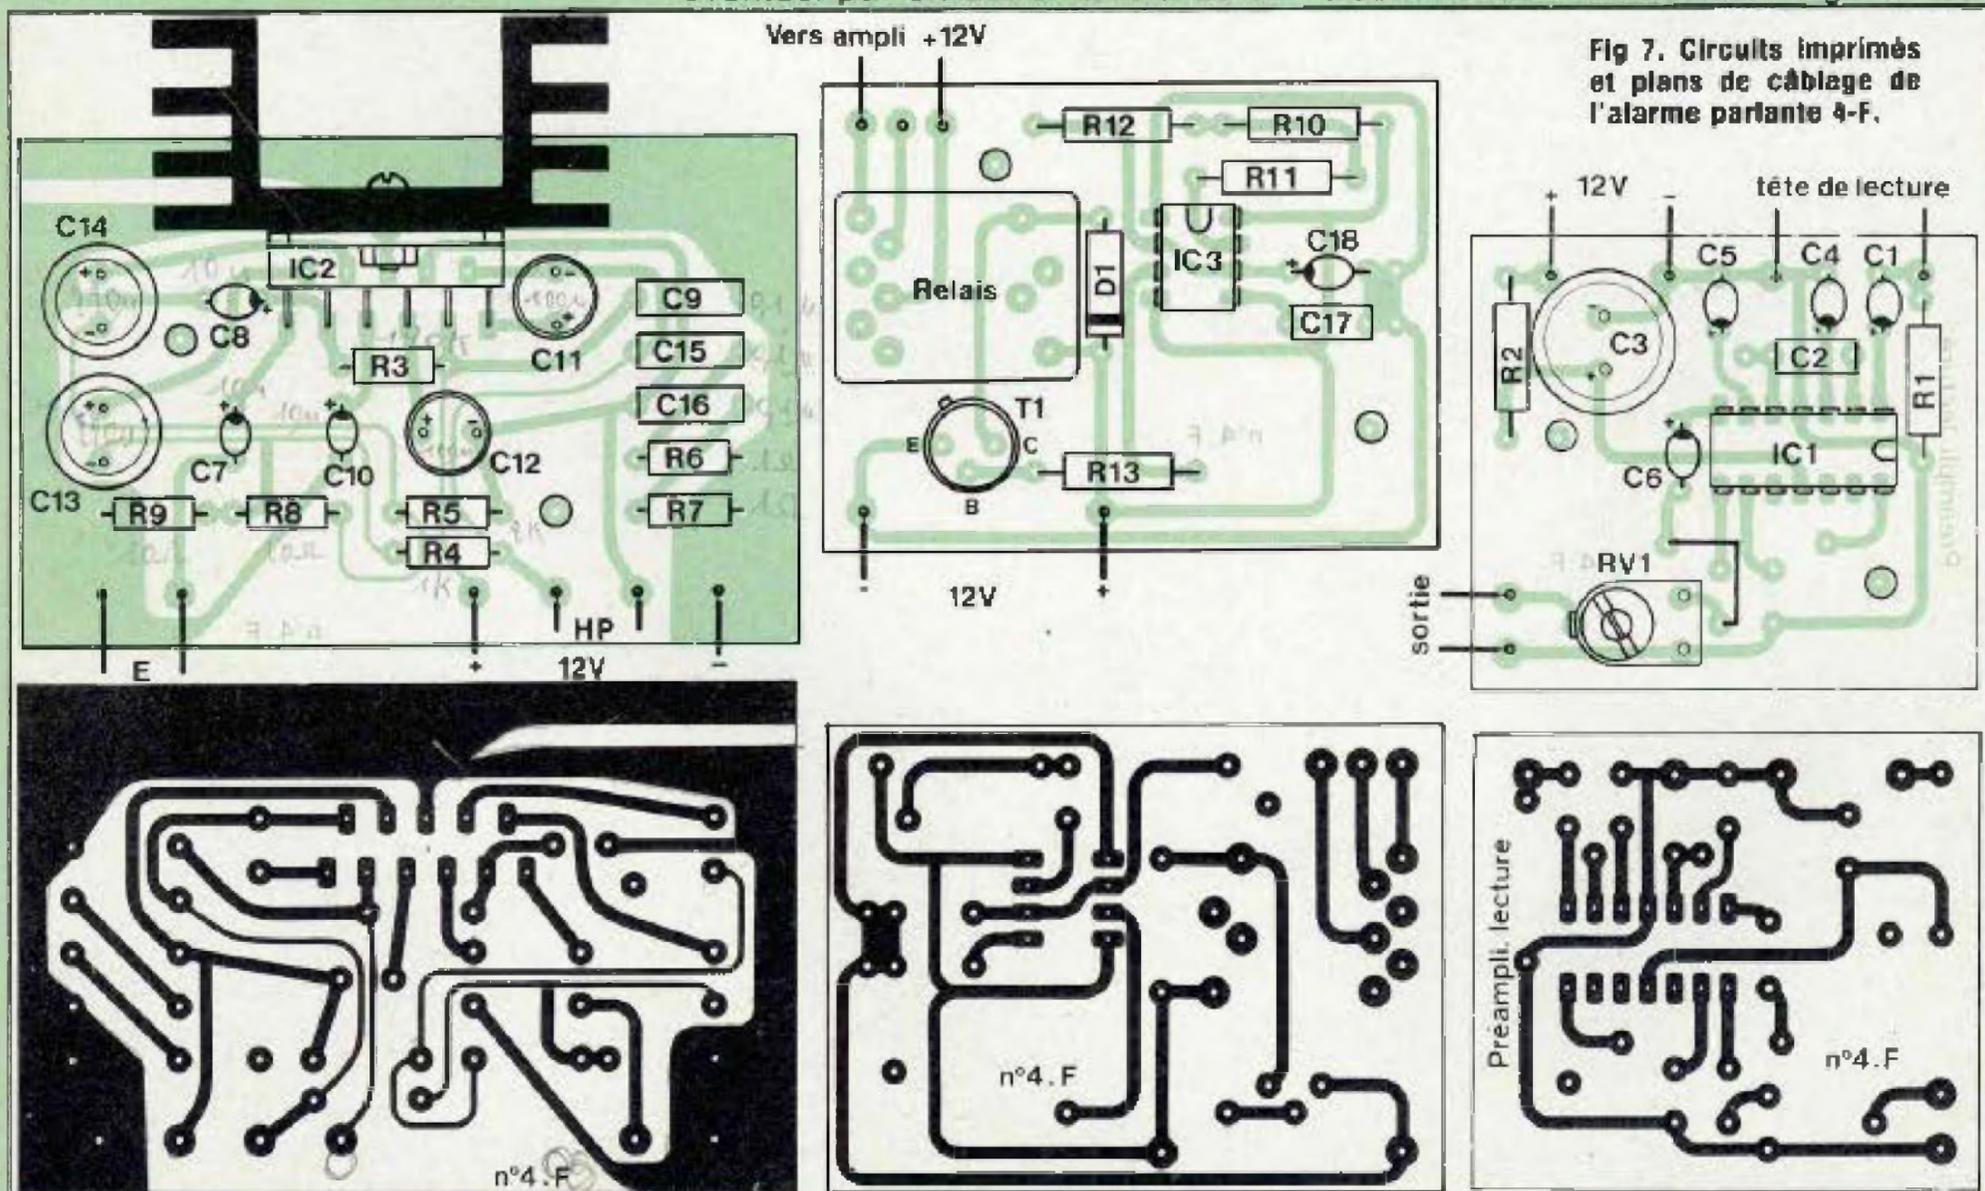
Circuits imprimés et plans de câblage de l'alarme parlante 4-F.
